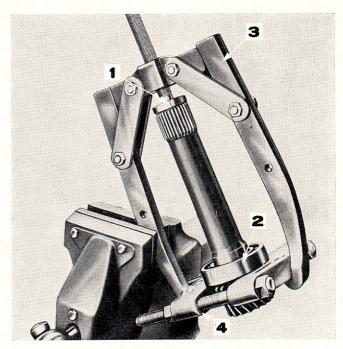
Dépose du roulement arrière d'arbre d'entrée de prise de force indépendante
